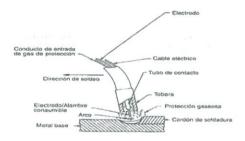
Soldadura por arco de metal y gas
